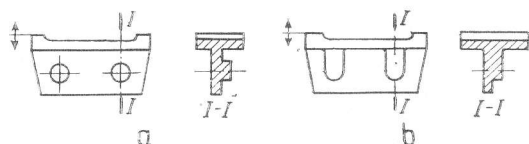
Plasarea bosajelor de către constructor pe piesa turnată:
